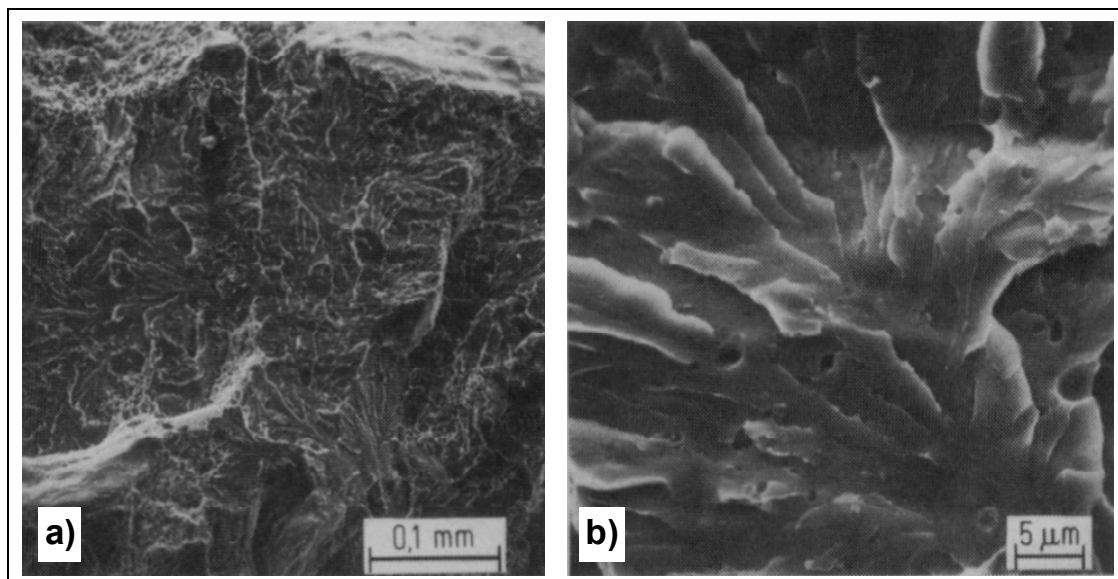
Fischauge in einer Schweißnaht [31]
